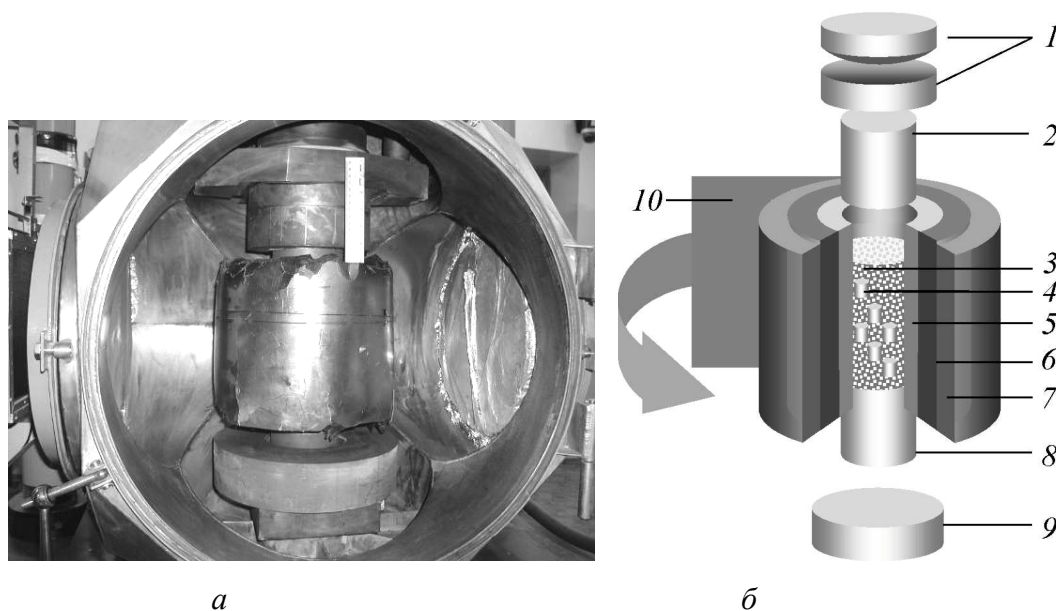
Внешний вид (а) и конструкция (б) пресс-формы: 1 – сферическая пара; 2, 8 – верхний и нижний пуансоны; 3 – порошковая передающая среда; 4 – преформы; 5 – графитовый цилиндр пресс-формы; 6 – УУКМ силовой цилиндр для упрочнения пресс-формы; 7 – графитовый войлок (теплоизоляция); 9 – нижняя опора; 10 – графитовая фольга
